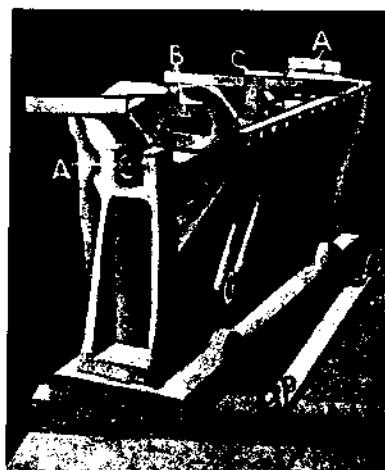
Приспособление для проверки положения гнезд подшипников.
